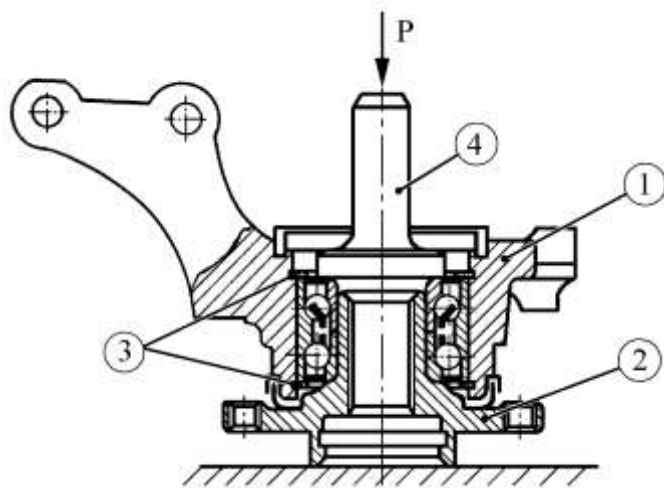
Напрессовка подшипника на ступицу переднего колеса:
